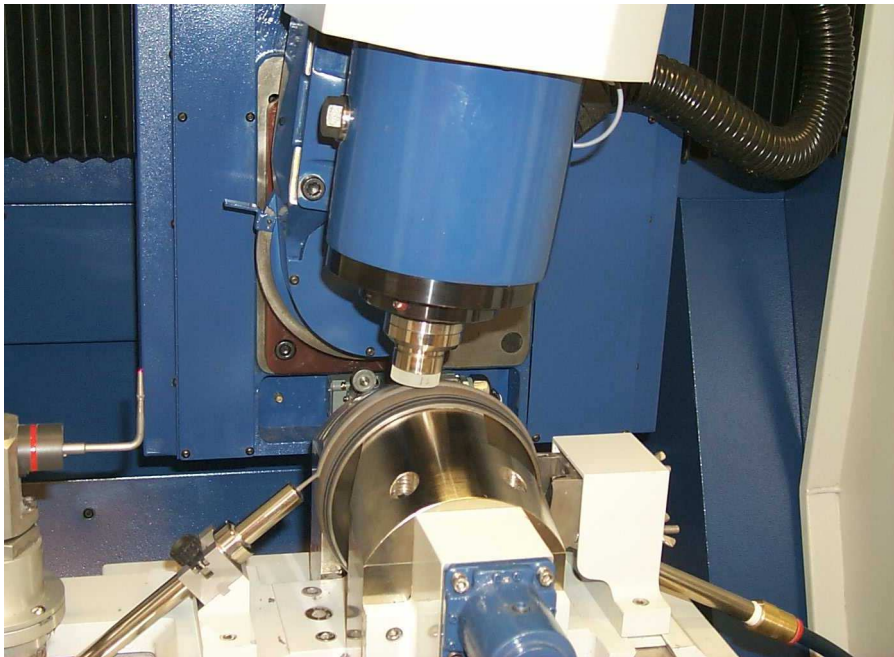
zone de travail de la machine Q22 de finition MRF pendant un polissage.
